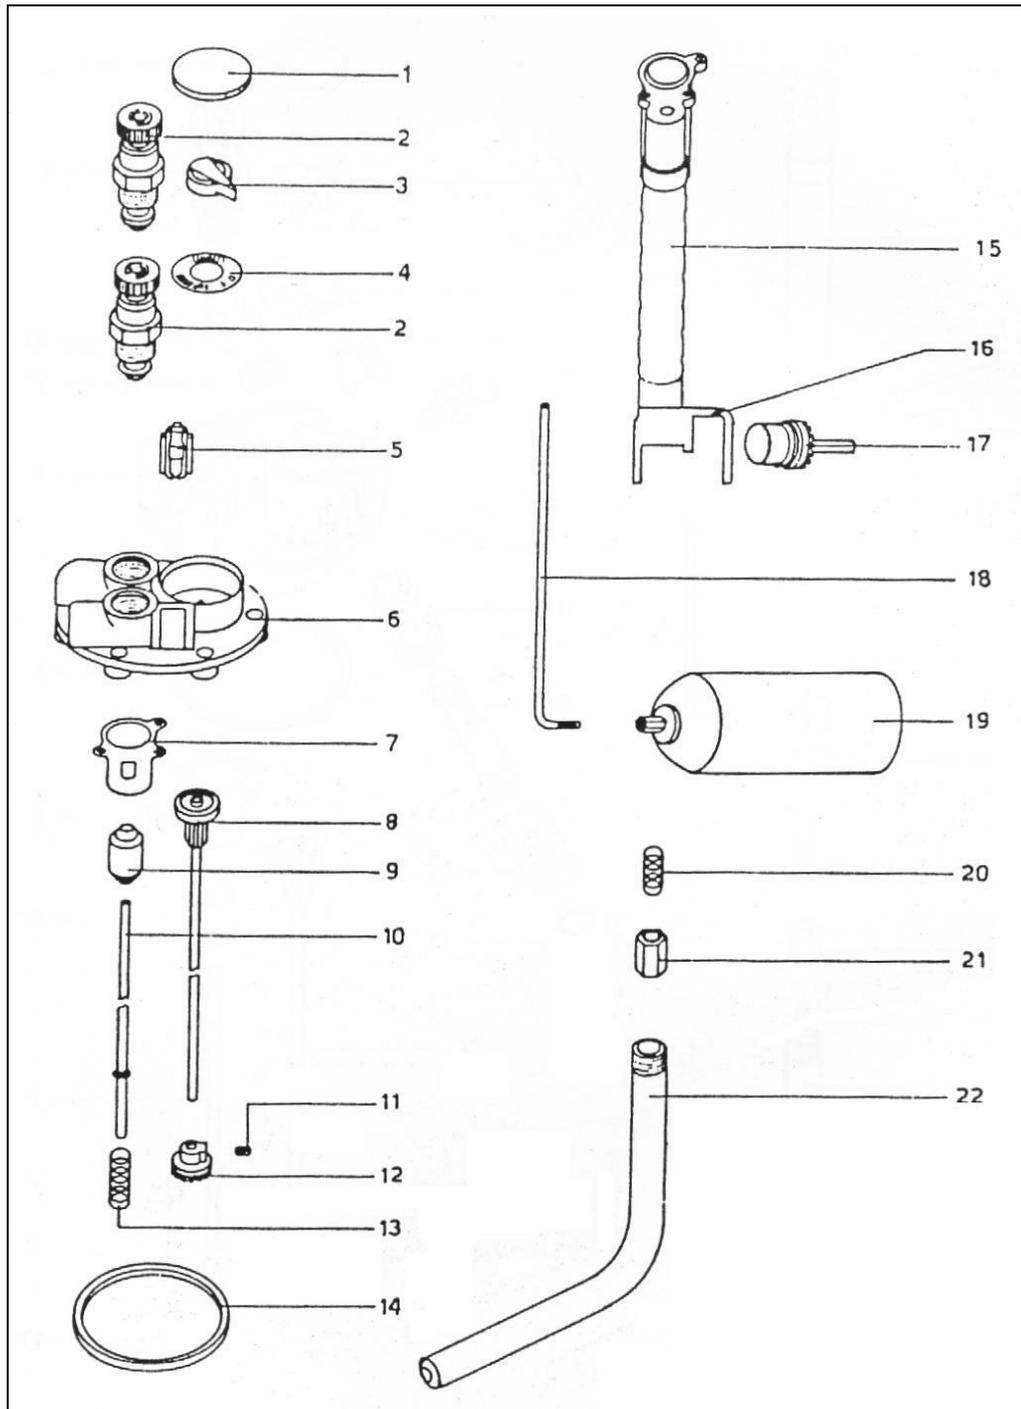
Esquema del despiece de la Multiválvula Minibloc
